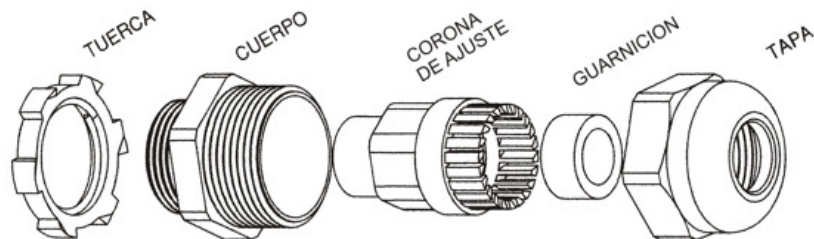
, DESPIECE DE PRENSA CABLES PLÁSTICO CON AJUSTE DE CORONA DENTADA
